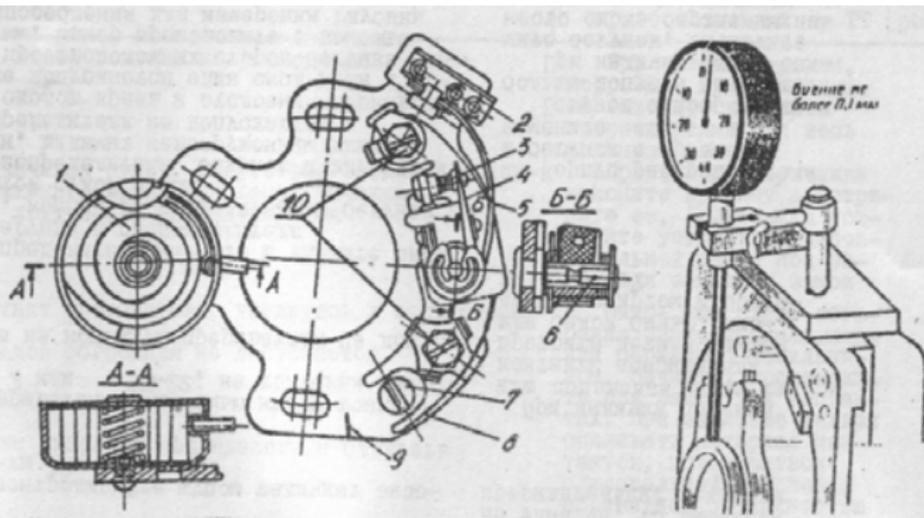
Пластика прерывателя: 1 - масленка; 2 - сухарь; 3 - контакты; 4 — рычажок; 5 - пружина; 6 — ось рычажка; 7 — эксцентрик; 8 -стойка контактная; 9 - риска регулировочная; 10 - винты
